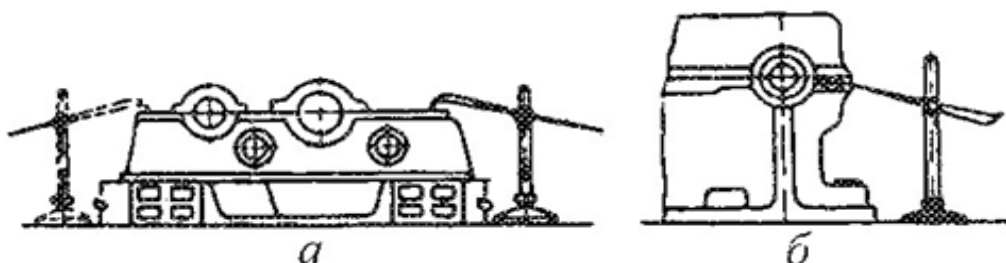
Вивіряння заготовок при обробці на розточувальних верстатах
